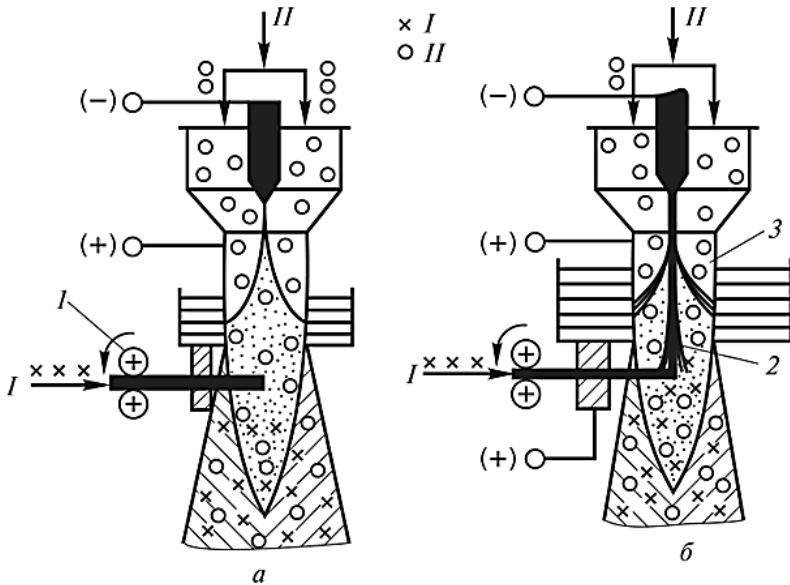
Схемы плазменного напыления расплавлением проволоки [16]:
